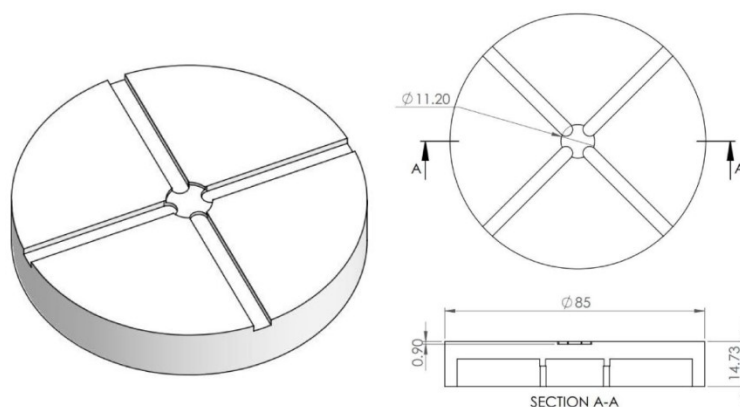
Чертеж съемного патрона-держателя спин-коатера Ossila Spin Coater
